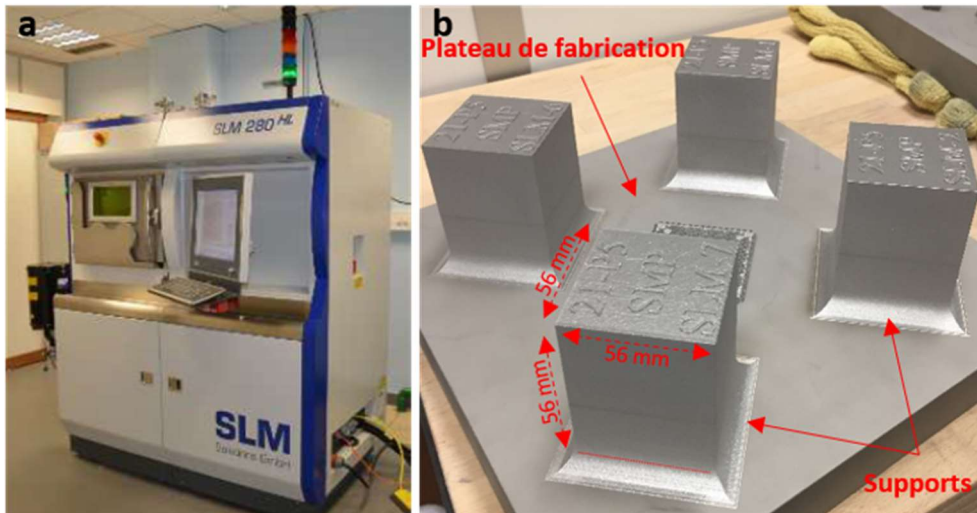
a) Machine de fusion laser sur lit de poudre SLM Solutions 280^{HL}, b) plateau de fabrication comprenant quatre cubes d'acier 316L à l'issue du procédé LPBF.
